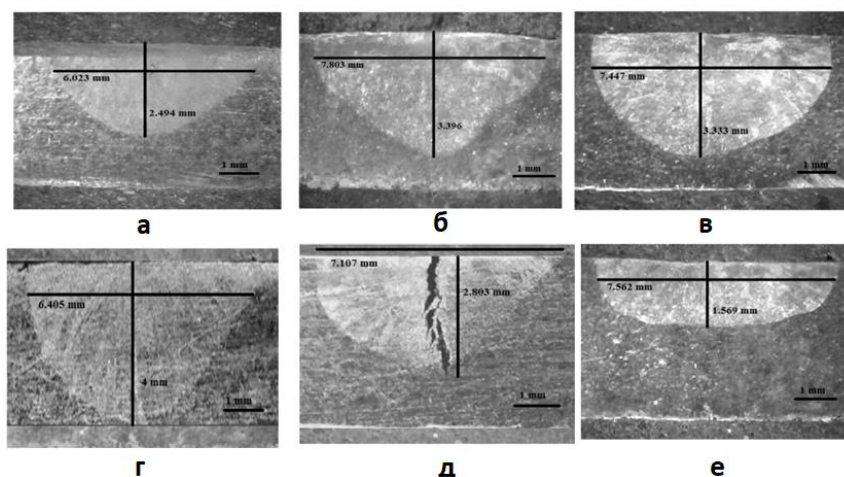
Микроструктуры образцов после сварки: а – TIG-сварка; б – А-TIG-сварка с V_2O_5 , в – А-TIG-сварка с Cr_2O_3 ; г – А-TIG-сварка с TiO_2 ; д – А-TIG-сварка с MoO_3 ; е – А-TIG-сварка с Al_2O_3
